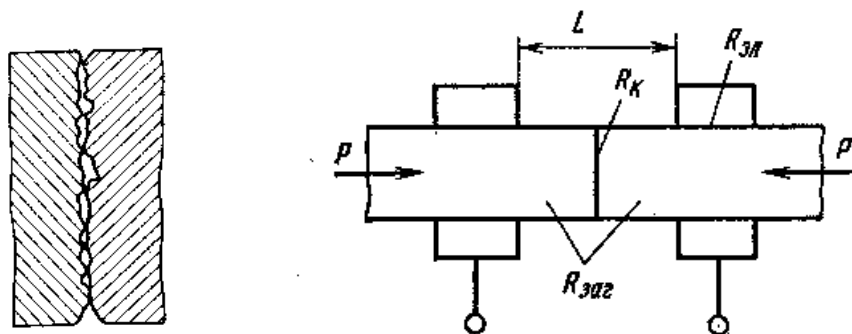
Схема стыковой контактной сварки
